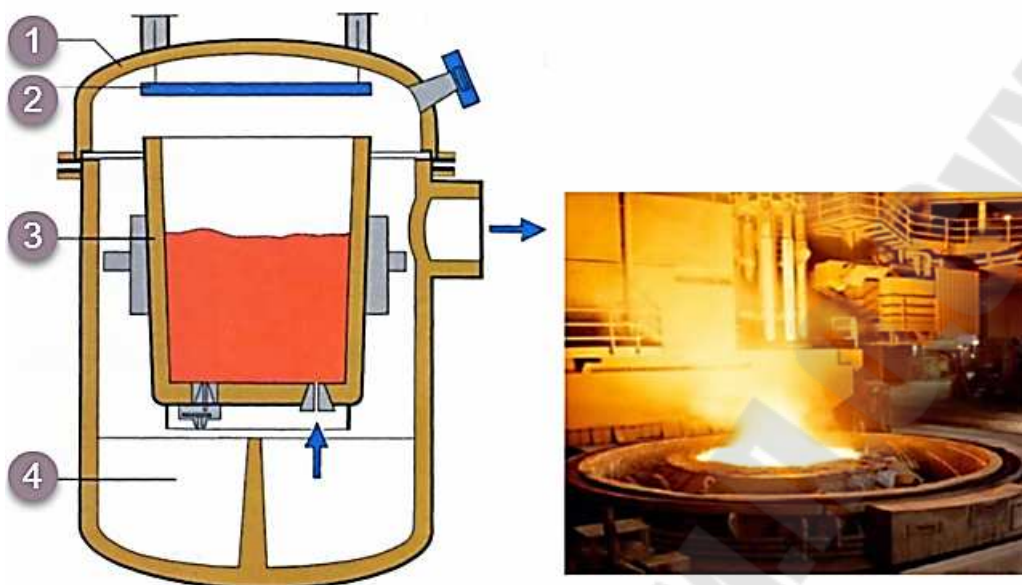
Установка для вакуумной обработки металла в ковше: 1 – вакуум-крышка; 2 – теплозащитный экран; 3 – сталеразливочный ковш; 4 – вакуум-камера
